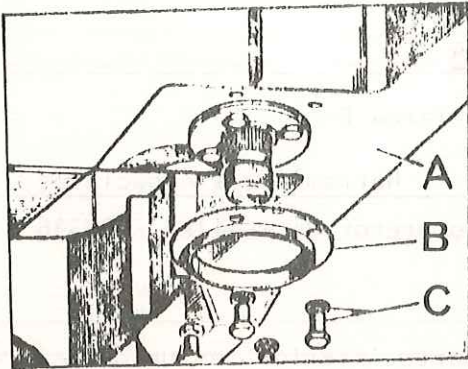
Placa-bridá para el montaje de la caja compensadora
